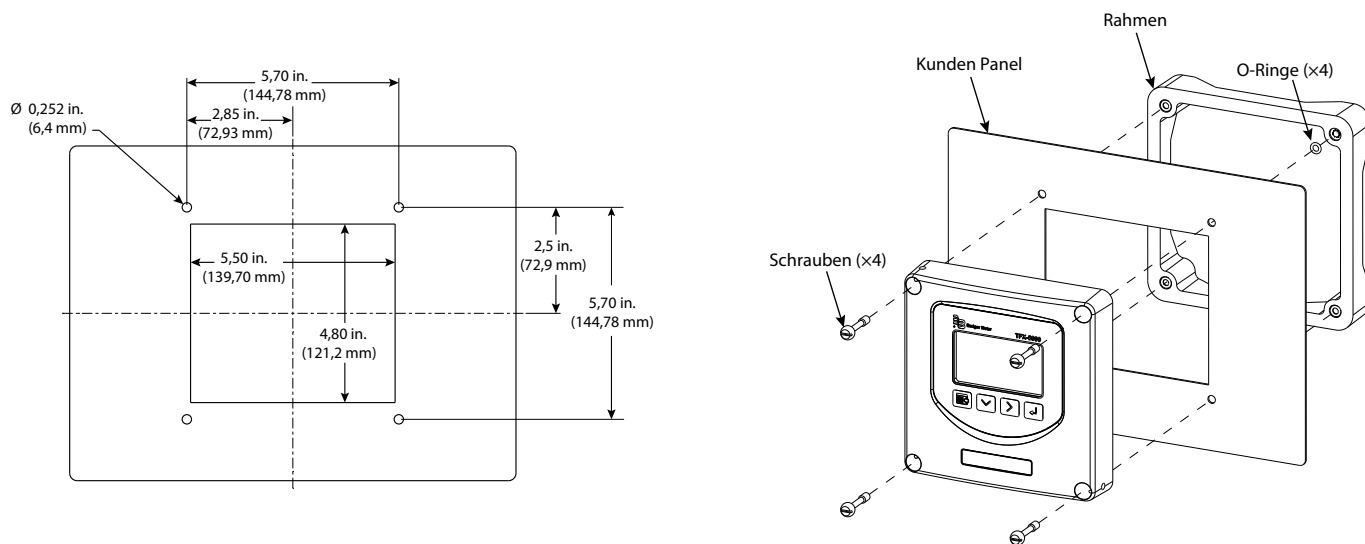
Abmessungen des Plattenausschnitts und Einbau-Explosionszeichnung
